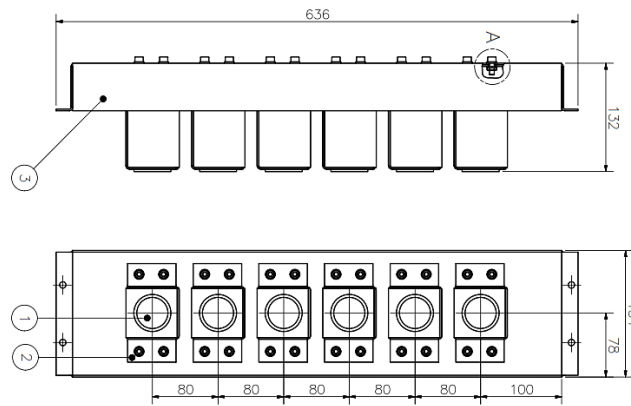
Arreglo de cámaras - Plano PE1.2.2-A3
